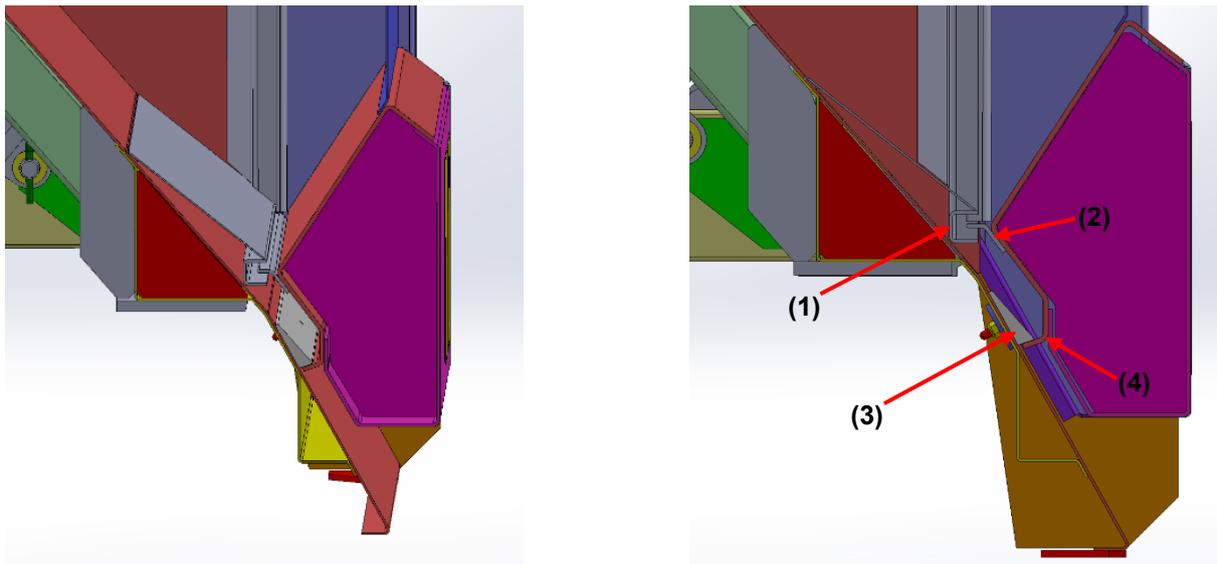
Detailansicht Dichtung RockTainer ORE (Planendach)
